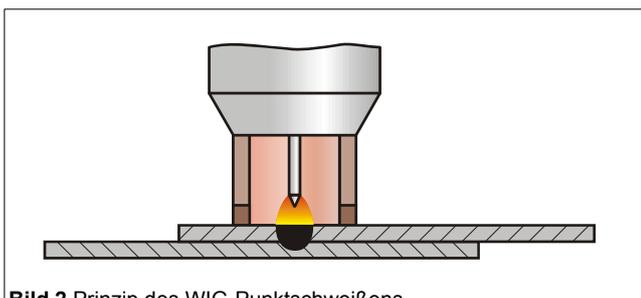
Prinzip des WIG-Punktschweißens
